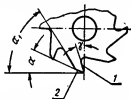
Цилиндрическая фреза с остроконечным зубом:
